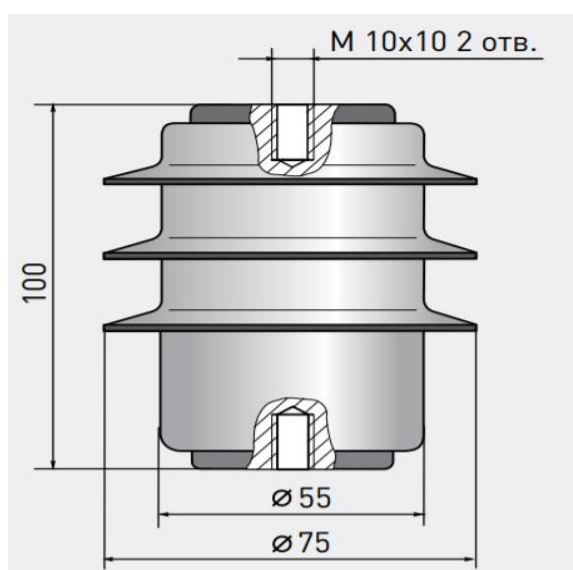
Общий вид ОПН-РТ 6/7,6
